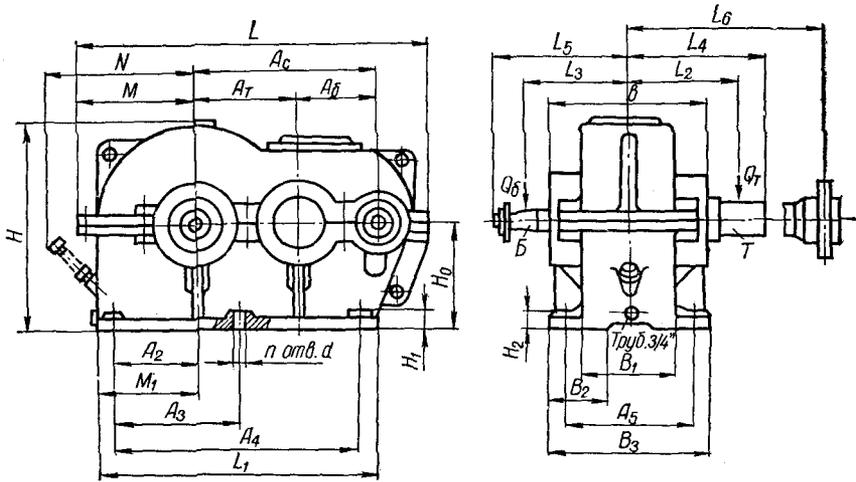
Основные и габаритные размеры редукторов РЦД.
